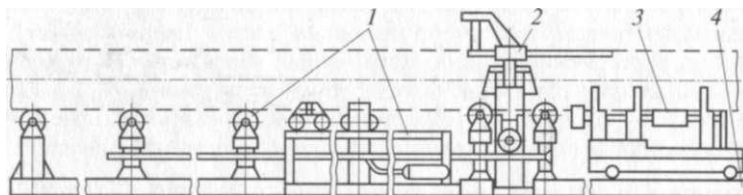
Установка УРТ-630М для газопламенной и плазменной резки труб:
